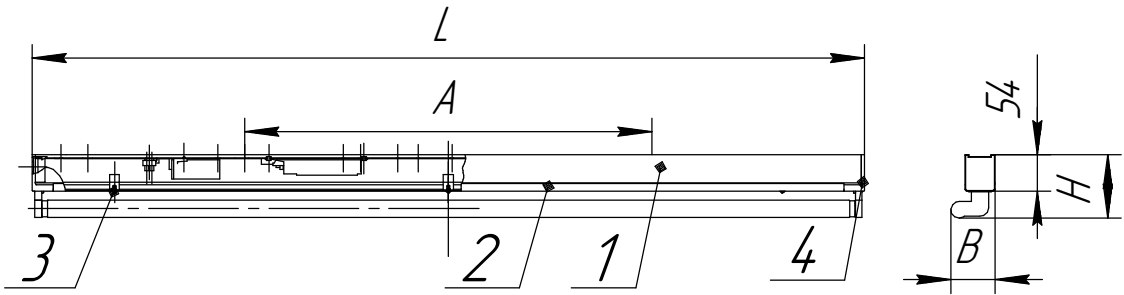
1. Корпус в сборе, 2. Крышка, 3. Винт, 4. Крышка.
